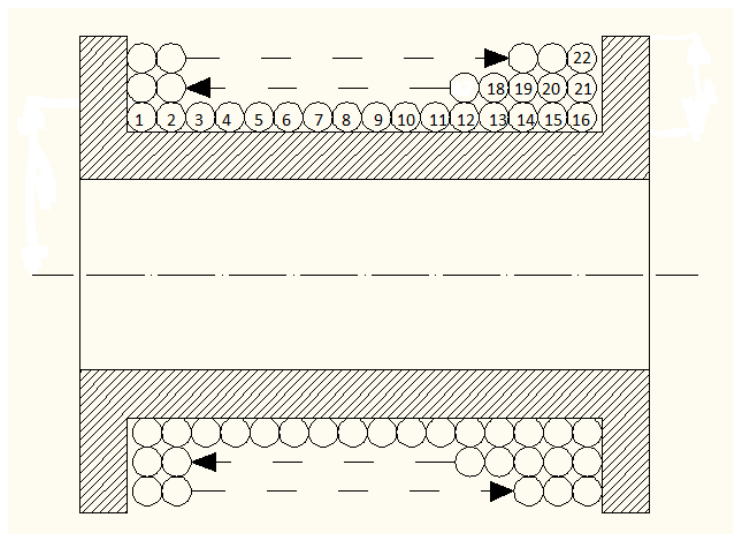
Bobină cilindrică multistrat (cu carcasă cu flanșă).
